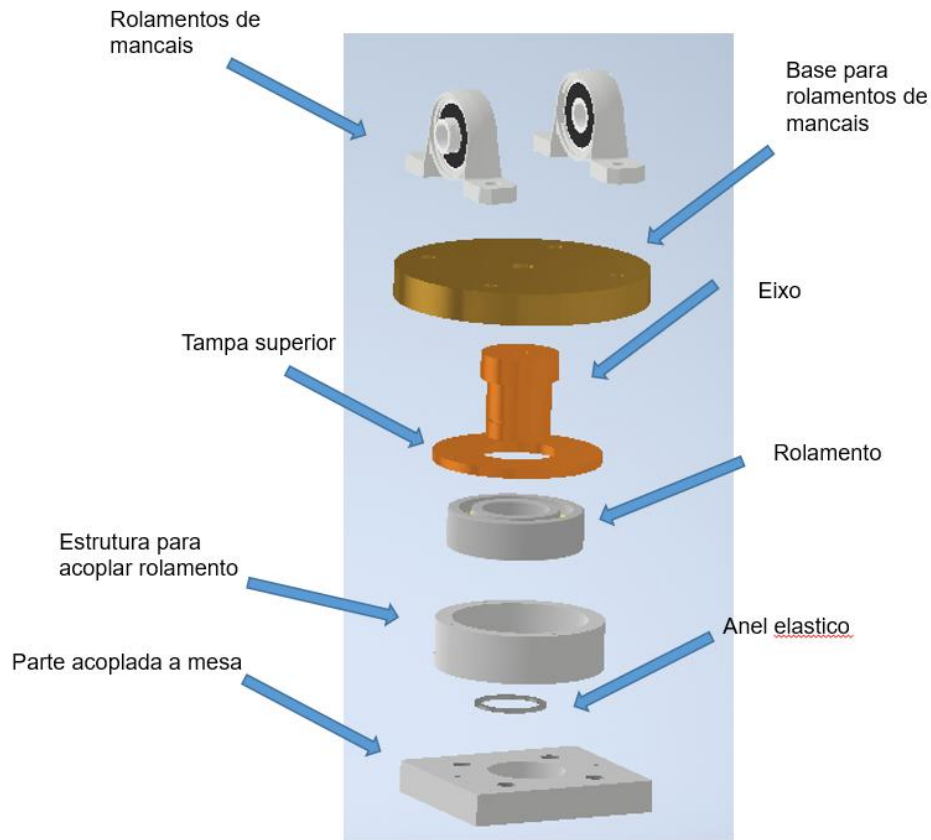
Conjunto de suporte do tubo cilíndrico
